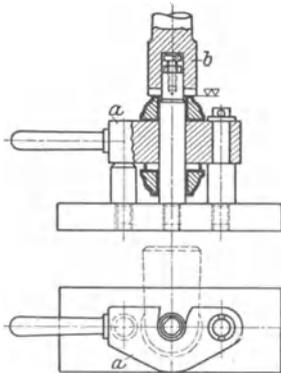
Standbohrspannvorrichtung mit Dornführung. *a* entfernensbestimmende Schwenksstütze. *b* Senkwerkzeug.
